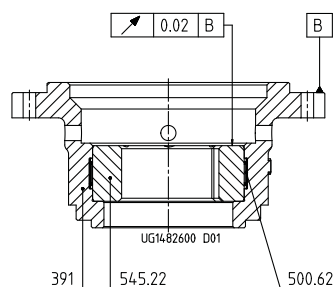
Проверить биение втулки подшипника относительно держателя кольца подшипника
